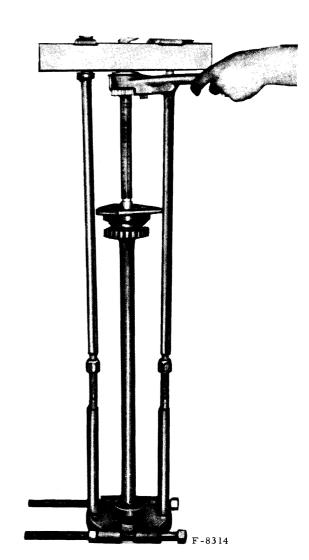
Montage du roulement sur l'arbre de prise de force arrière.
